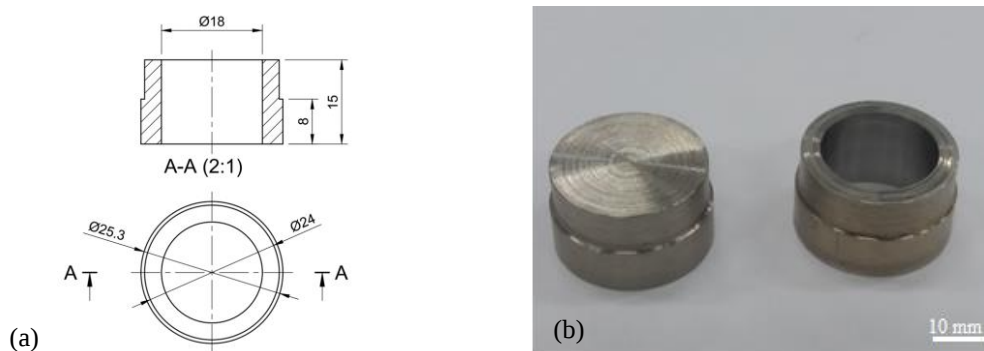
Fotos do: (a) desenho da peça e (b) corpo de prova e da peça usinada. Fonte: própria
